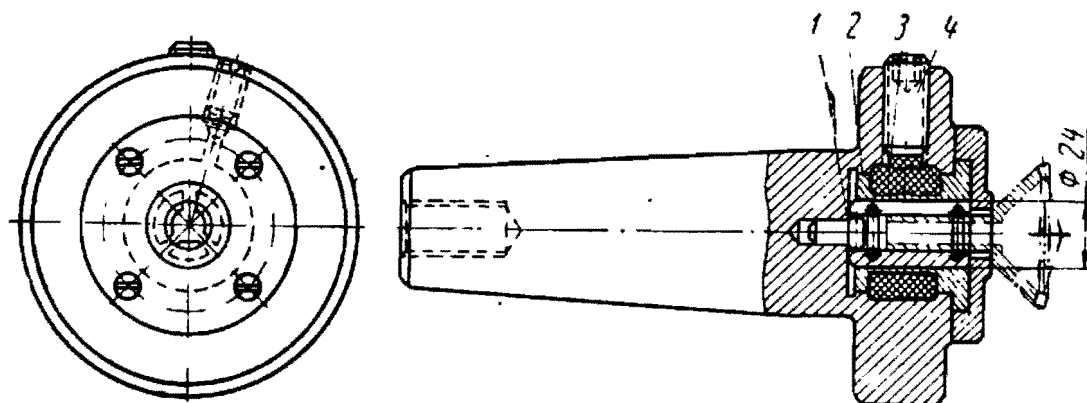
Оправка для установки и закрепления заготовок на зубострогальном станке
